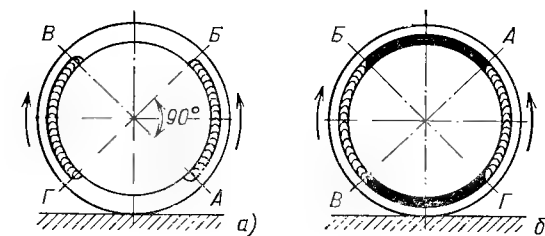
Порядок выполнения сварки стыка труб с поворотом на 180°.
